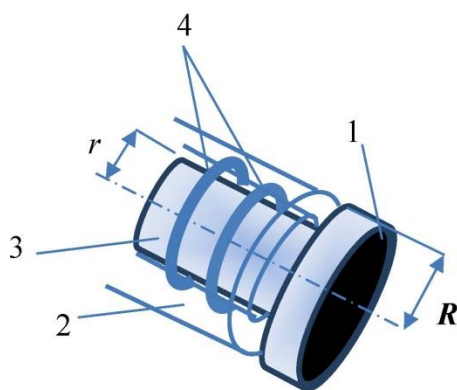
Конструкция вращающихся вокруг своего центра резцов типа PDC: 1 – резец PDC; 2 – корпус; 3 – ось; 4 – стопорные упругие кольца
